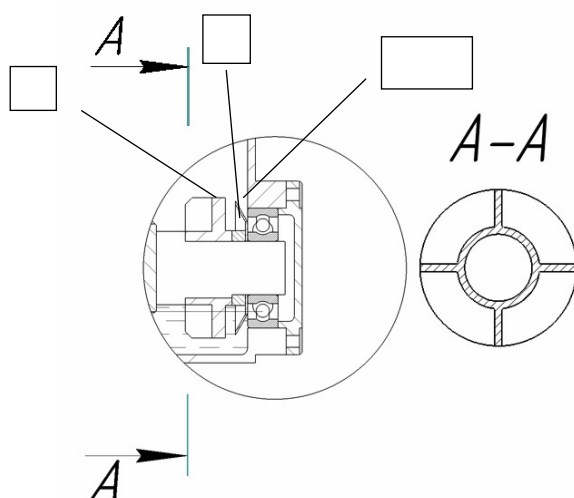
Компоновка подшипникового узла быстроходного вала:
